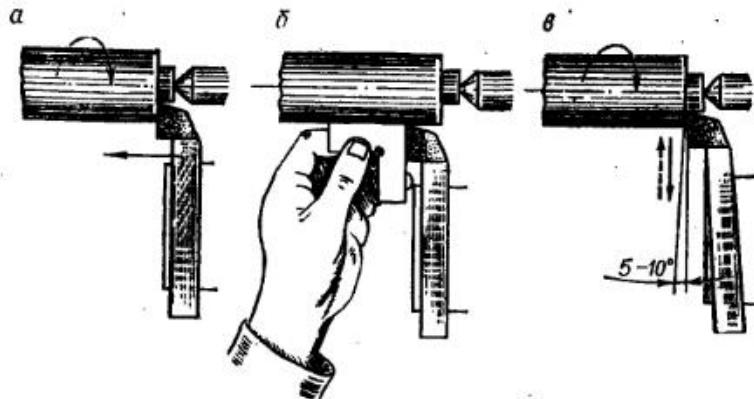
Положение резцов при обработке ступенчатых поверхностей
